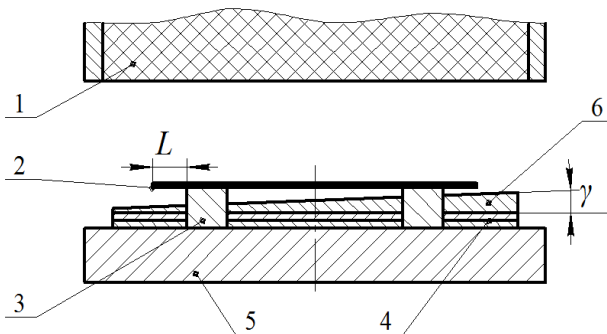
Вирізний шаблон, зменшений за допомогою набору пластин:
